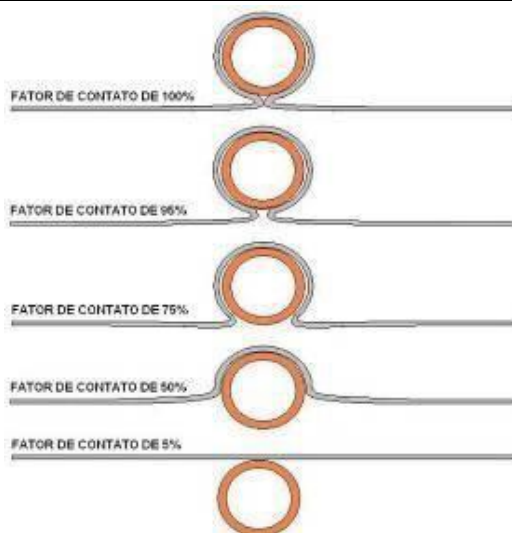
Exemplos de fator de contato entre Placa Absorvedora e Serpentina
